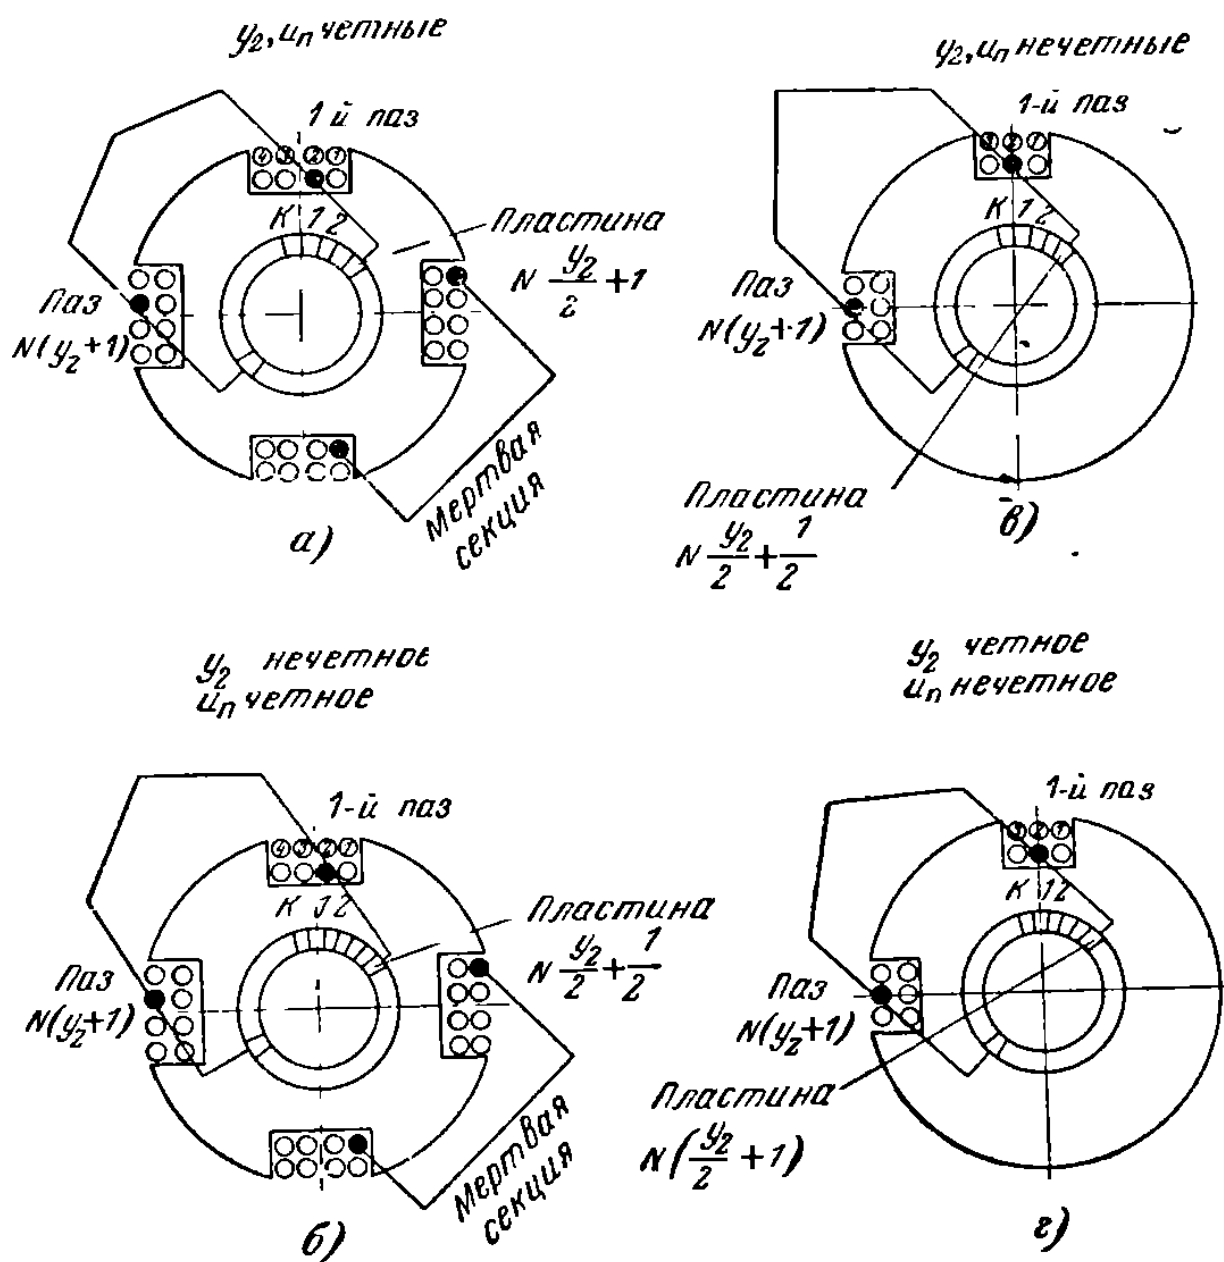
Схемы разметки якоря с волновой обмоткой.
